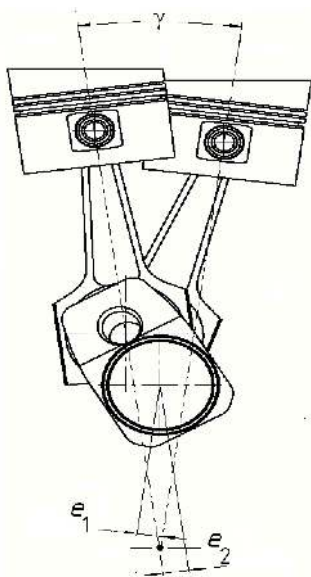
Конструктивная схема двухцилиндрового отсека VR-двигателя
